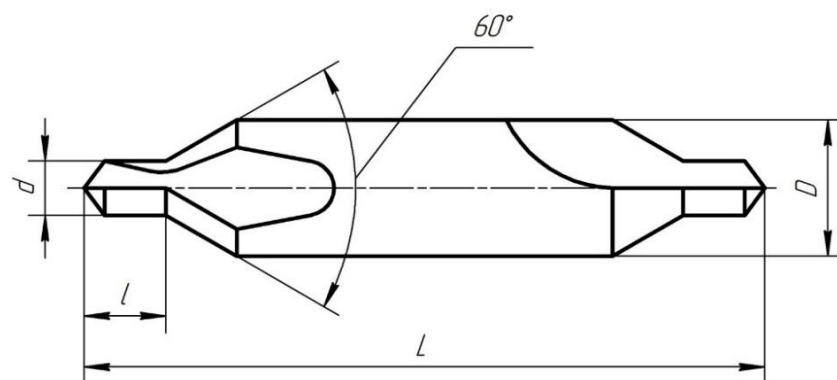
Центровочное сверло без предохранительного конуса
